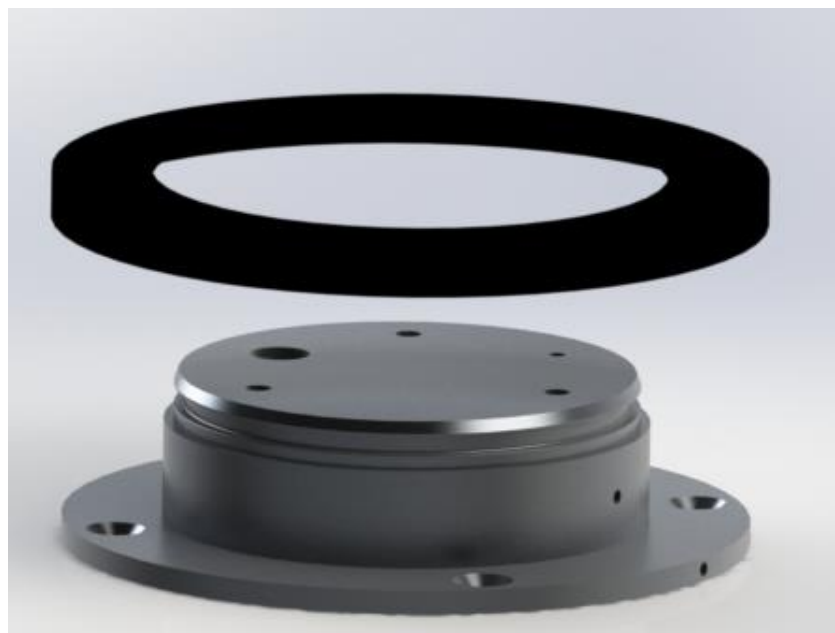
Explosionado conjunto base (Fuente: propia)
